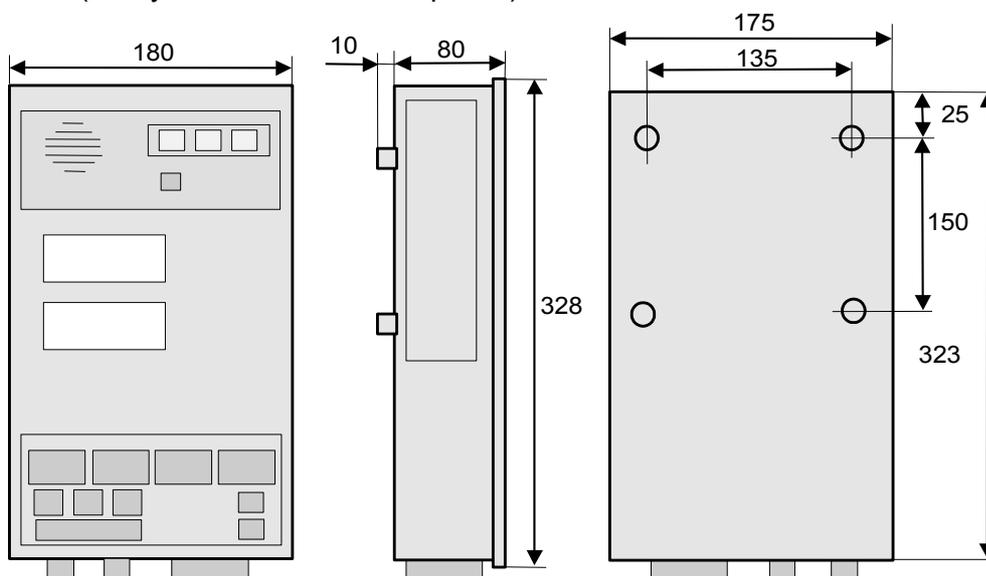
Габаритные и присоединительные размеры БОДа
